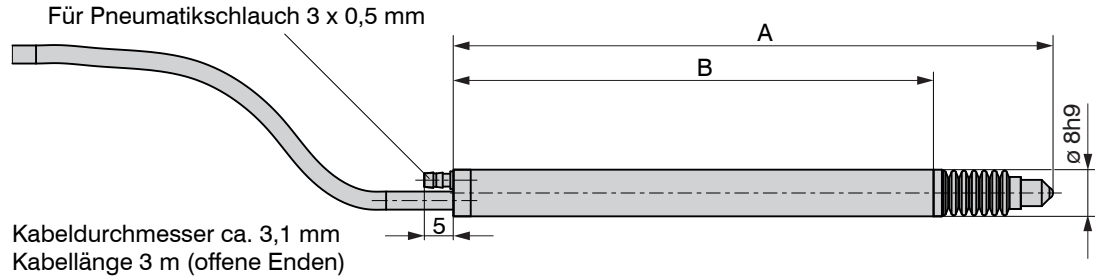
Gehäusemaße für Messtaster DTA-xG8-3-CA-V
